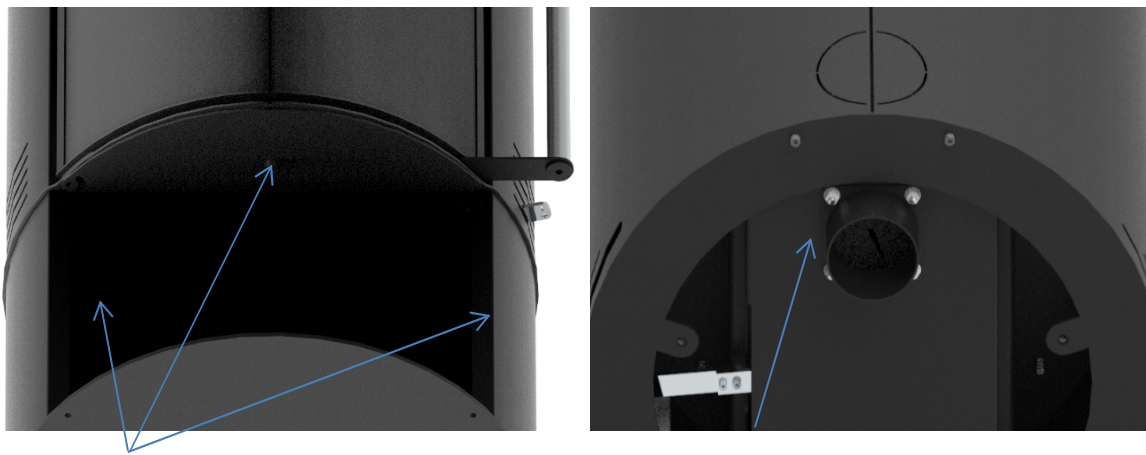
Entrada de aire exterior, (M) sección (M) a retirar para la entrada de aire exterior
